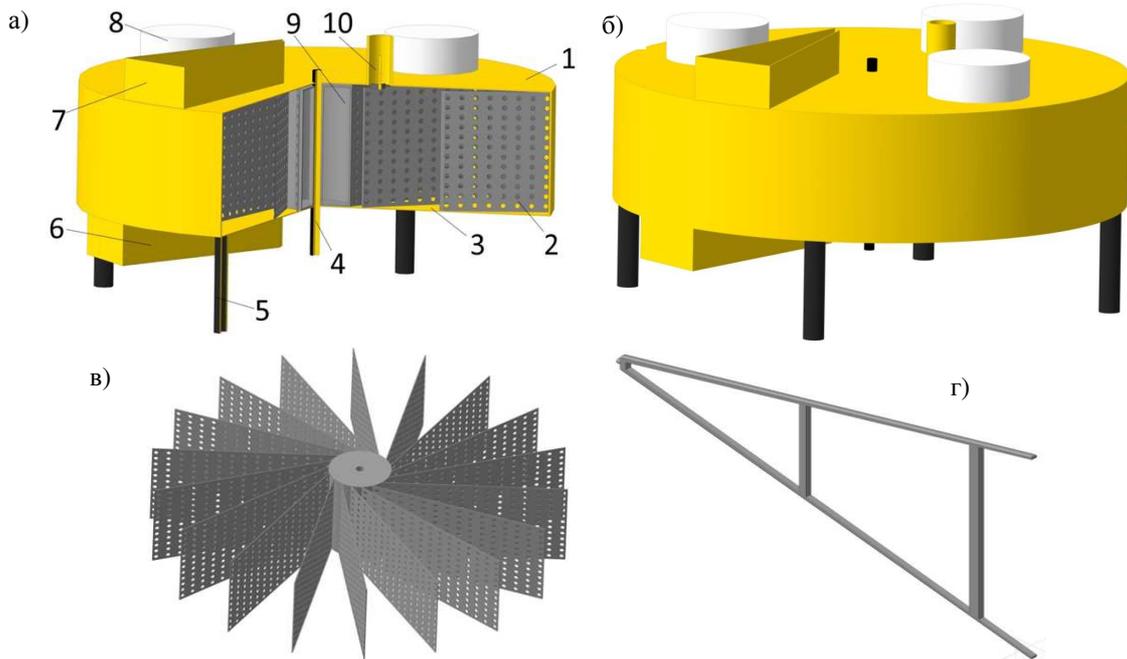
Микроволновая сушилка пушно-мехового сырья роторного типа: а) пространственное изображение сушилки (в разрезе); б) сушилка, вид спереди; в) неферромагнитный ротор с перфорированными отсеками; г) правилка для пушно-мехового сырья; 1 – цилиндрический экранирующий корпус; 2 – неферромагнитный ротор с перфорированными отсеками; 3 – резонаторы с трапецидальным сечением; 4 – вал барабана, соединенный с электродвигателем; 5 – монтажный каркас; 6 – выгрузной патрубок (запредельный волновод); 7 – загрузочный патрубок (запредельный волновод); 8 – сверхвысокочастотные генераторы; 9 – барабан из неферромагнитного материала; 10 – вытяжной вентилятор.
